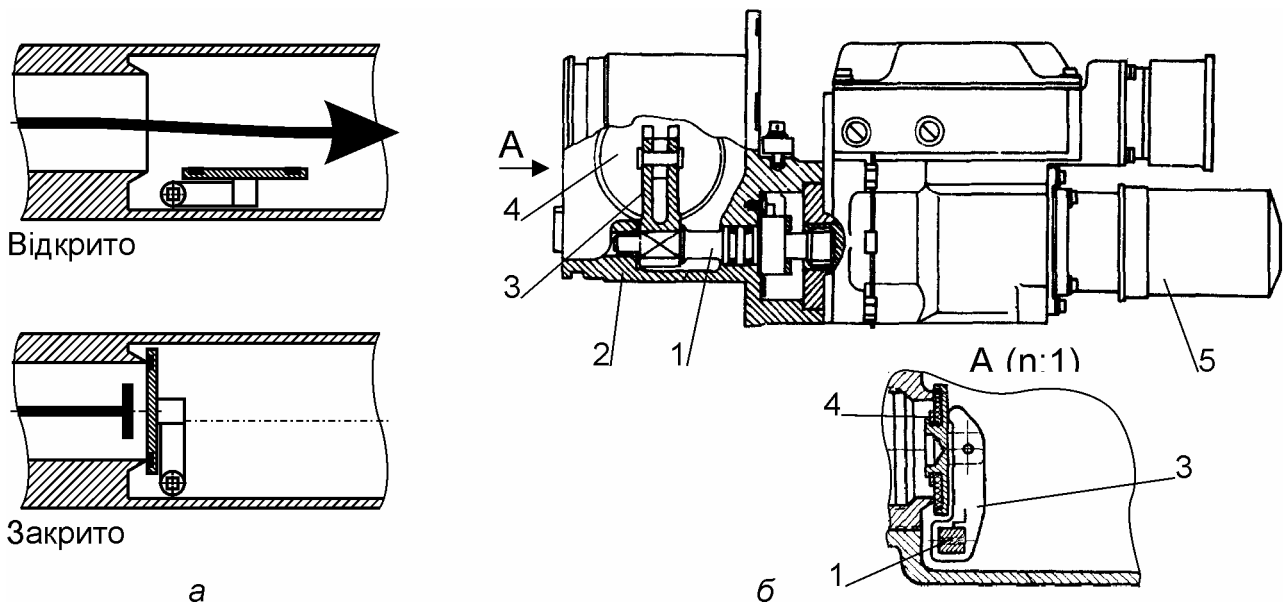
Тарілчастий кран 771300: а — схема роботи; б — конструкція; 1 — вал; 2 — корпус; 3 — важіль; 4 — тарілка; 5 — електромеханізм
